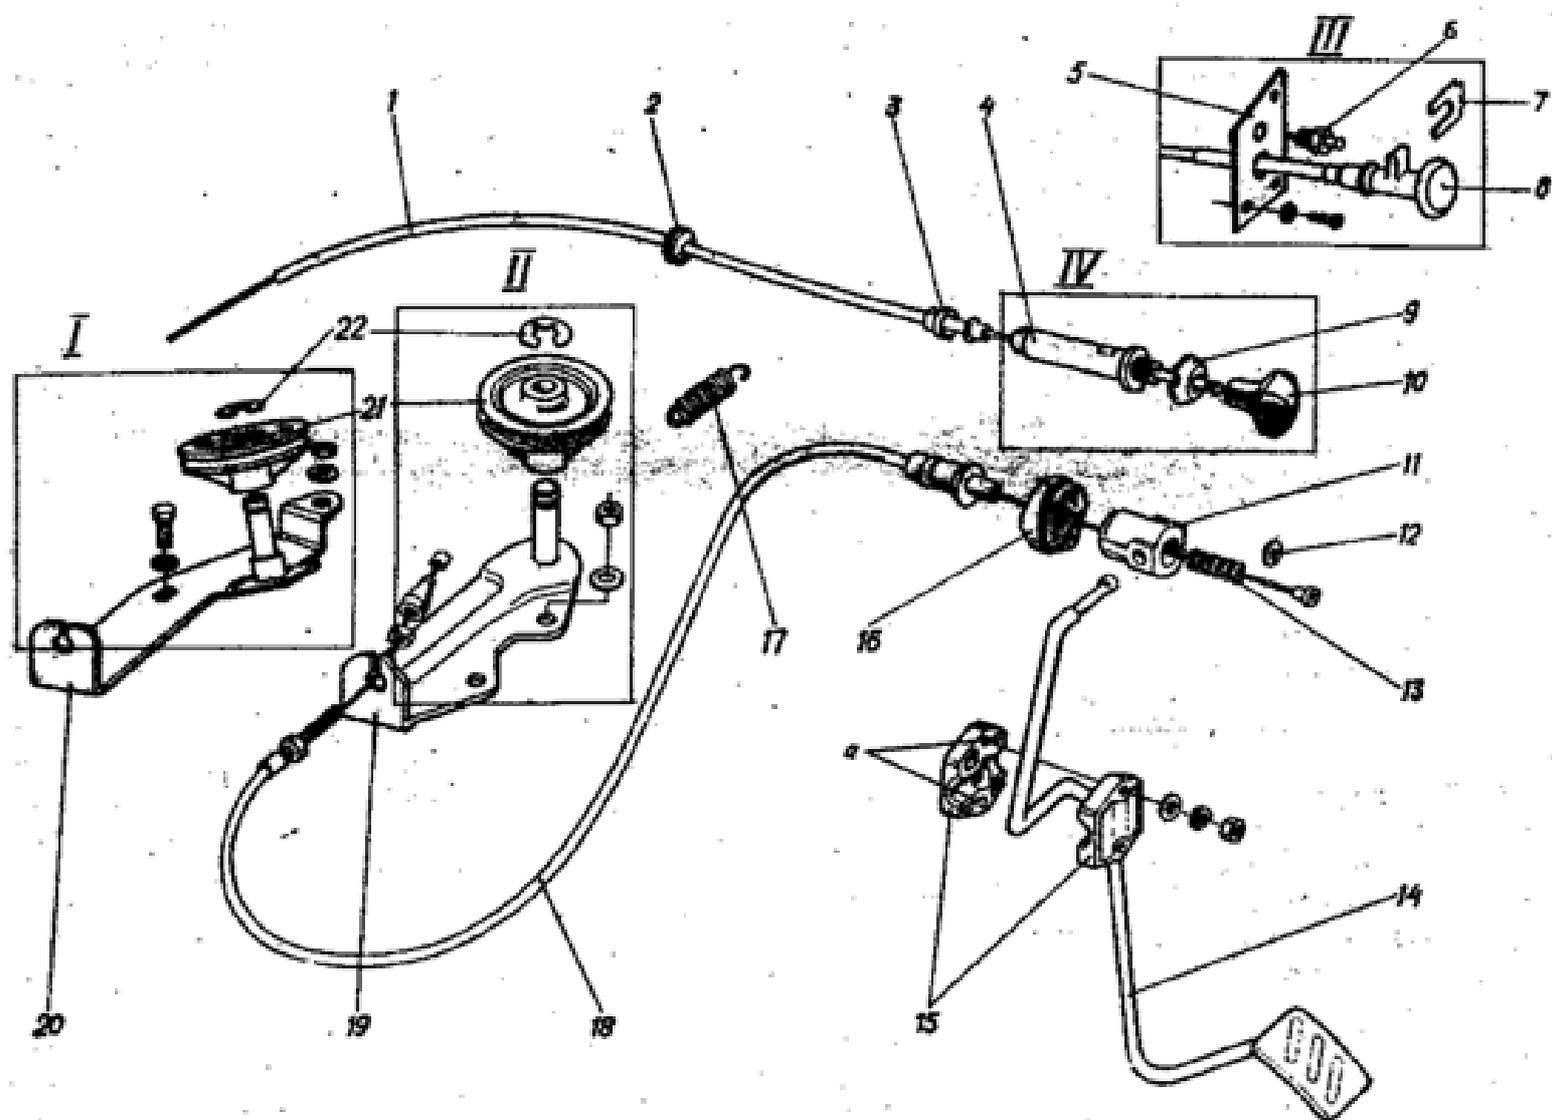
Детали привода карбюратора и их крепление: 1 - оболочка тяги воздушной заслонки; 2 - втулка уплотнительная; 3 - фиксатор; 4 - кронштейн; 5 - кронштейн выключателя; 6 - выключатель; 7 - скоба; 8 - ручка; 9 - гайка; 10 - ручка; 11 - корпус компенсатора; 12 - фиксатор тяги; 13 - пружина компенсационная; 14 - педаль акселератора; 15 - опора; 16 - упор; 17 - пружина; 18 - тяга дроссельной заслонки в сборе; 19 - кронштейн (для карбюратора ДААЗ 21081-1107010); 20 - кронштейн (для карбюратора К-126Л); 21 - шкив; 22 - кольцо стопорное; I - установка кронштейна с карбюратором К-126Л; II - установка кронштейна с карбюратором ДААЗ 21081-1107010
